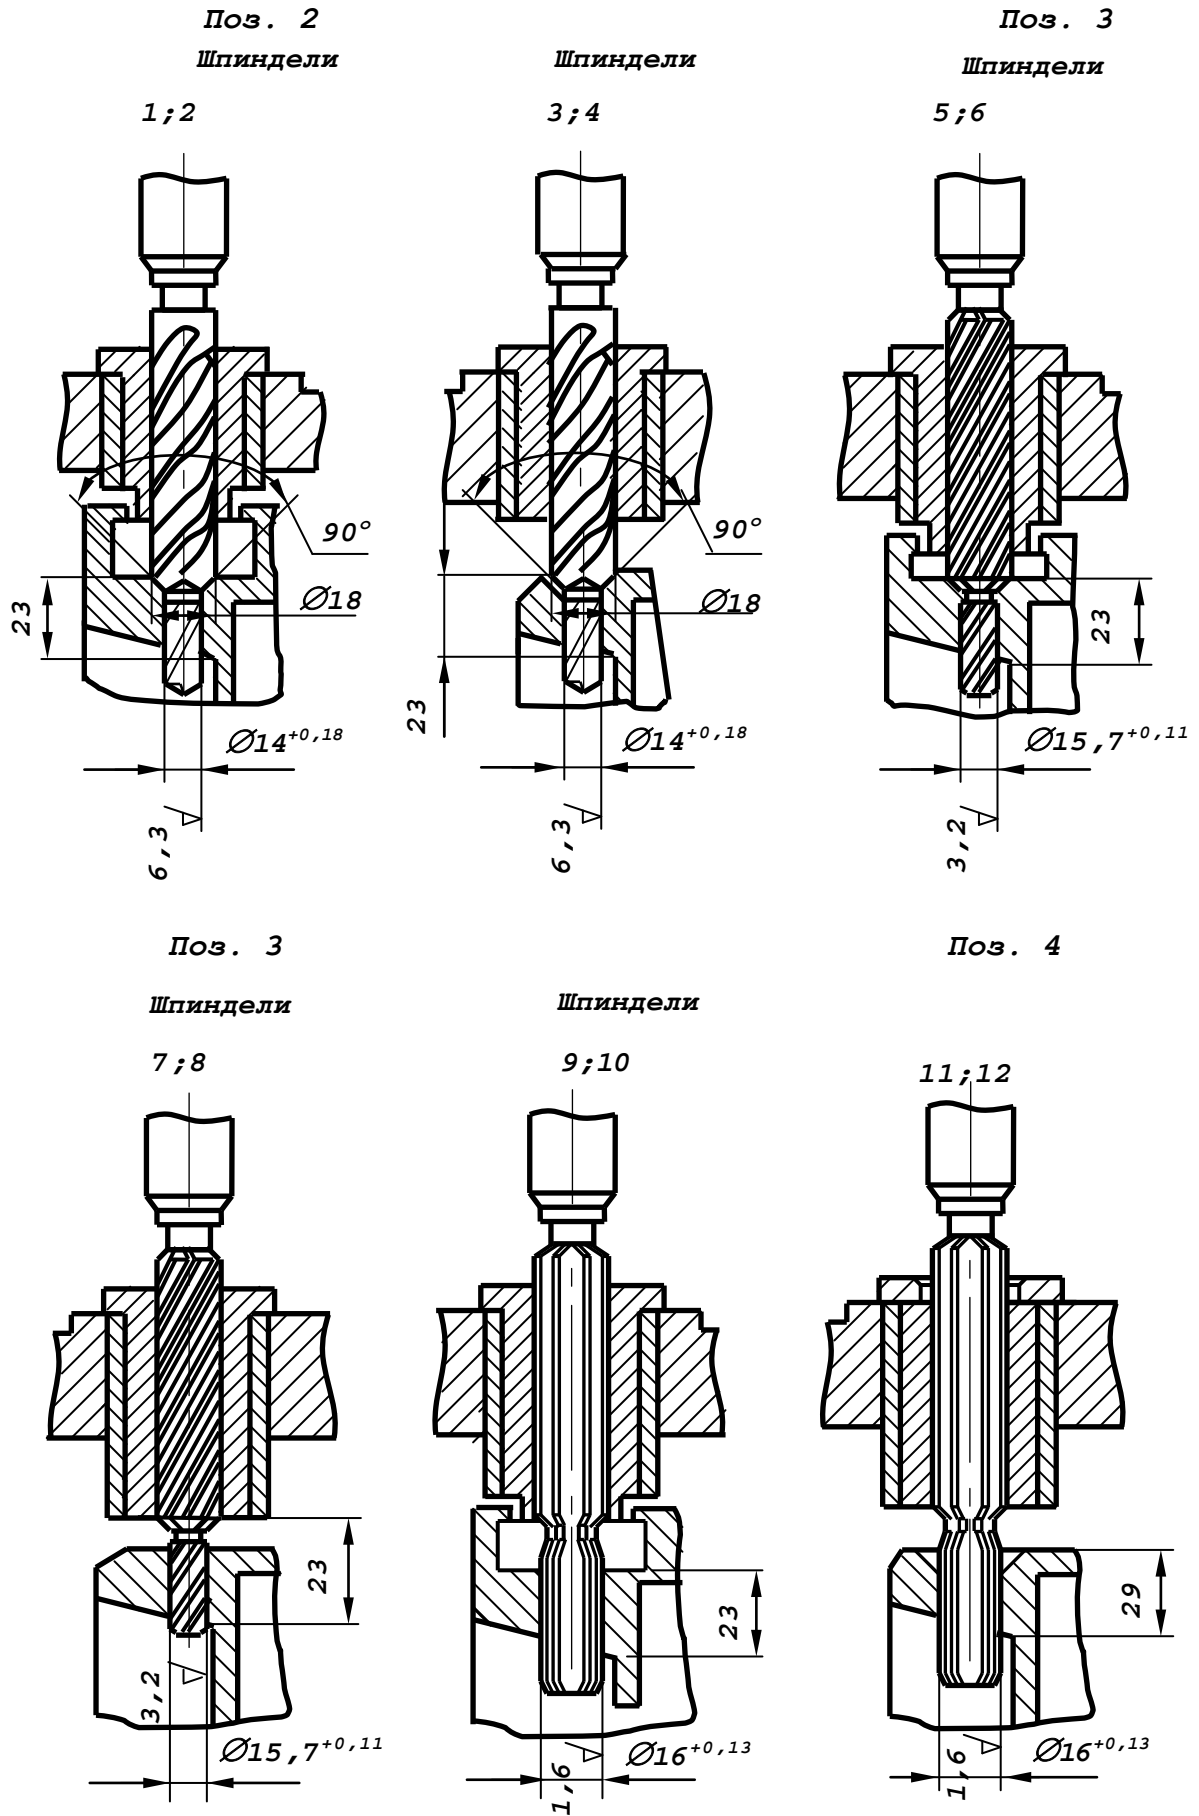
Эскиз наладки 12-шпиндельного агрегатного вертикально-сверлильного станка
